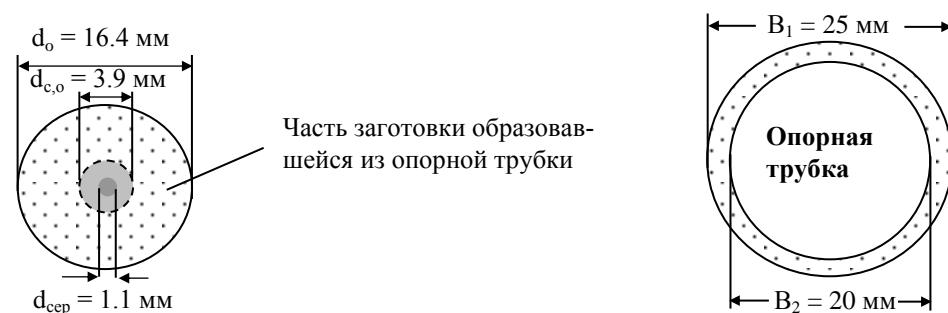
Опорная трубка и образованная с её помощью заготовка для SM волокна.
